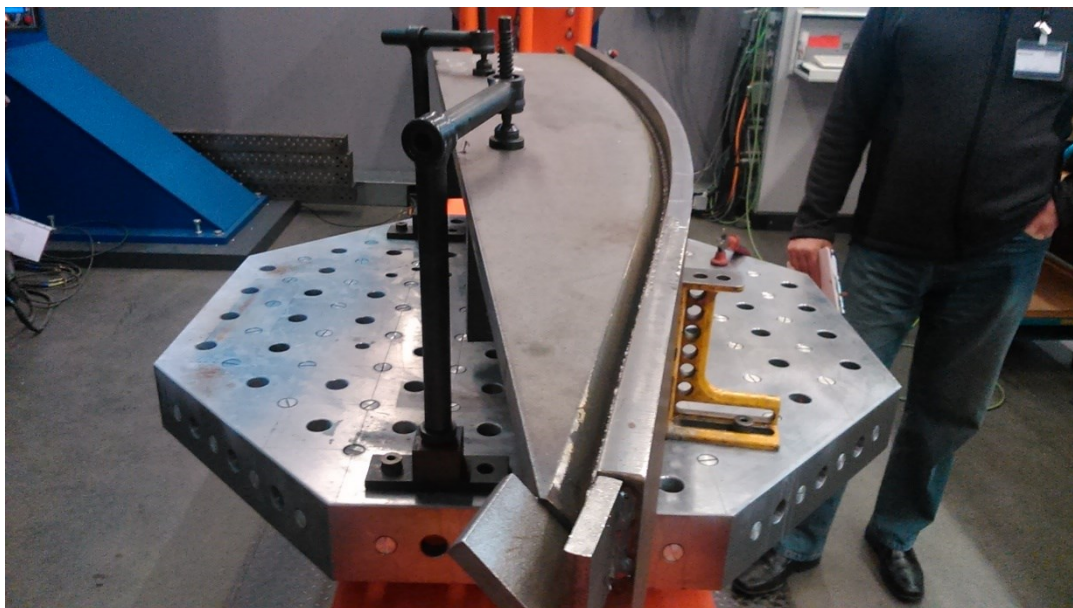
Zkouška „A“ po zavaření použitím technologie Tandem Weld
